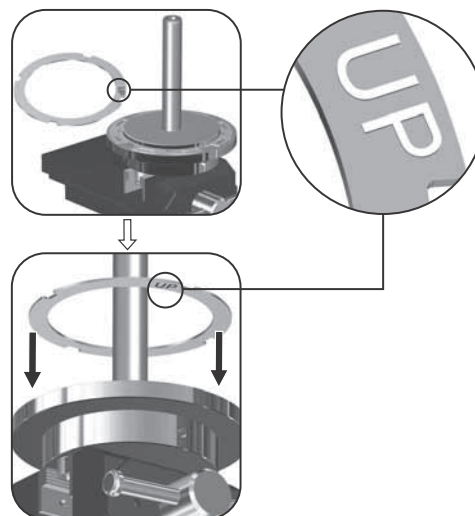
Установка уплотнительного кольца (45) с надписью «UP» (ВВЕРХ), указывающей вниз, в направлении стопора уплотнительного кольца (65)
